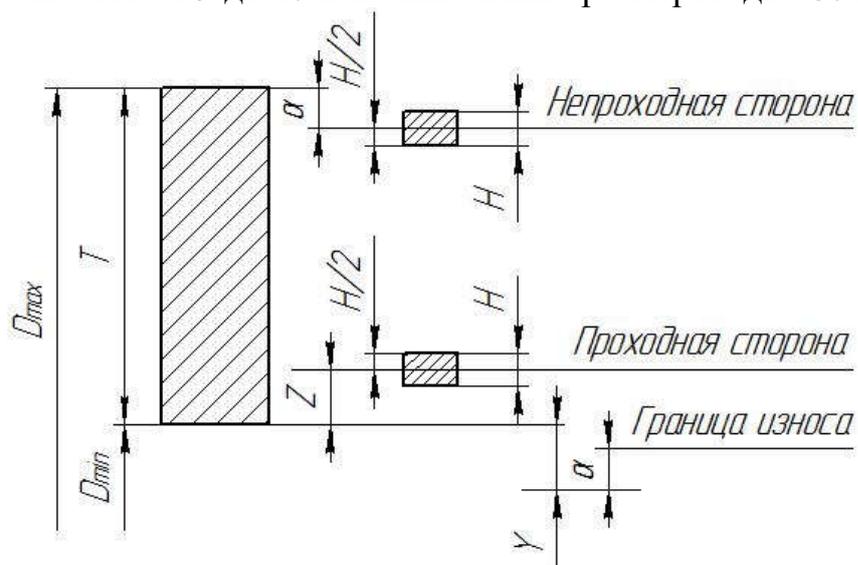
Расположение интервалов допусков для контроля отверстий квалитетов 6, 7, 8 и номинальным размером свыше 180 мм
